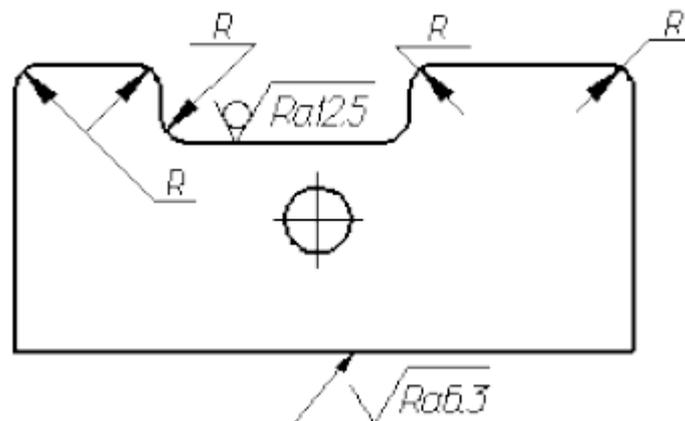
Пример обозначения шероховатости поверхности плавно переходящей одна в другую.
